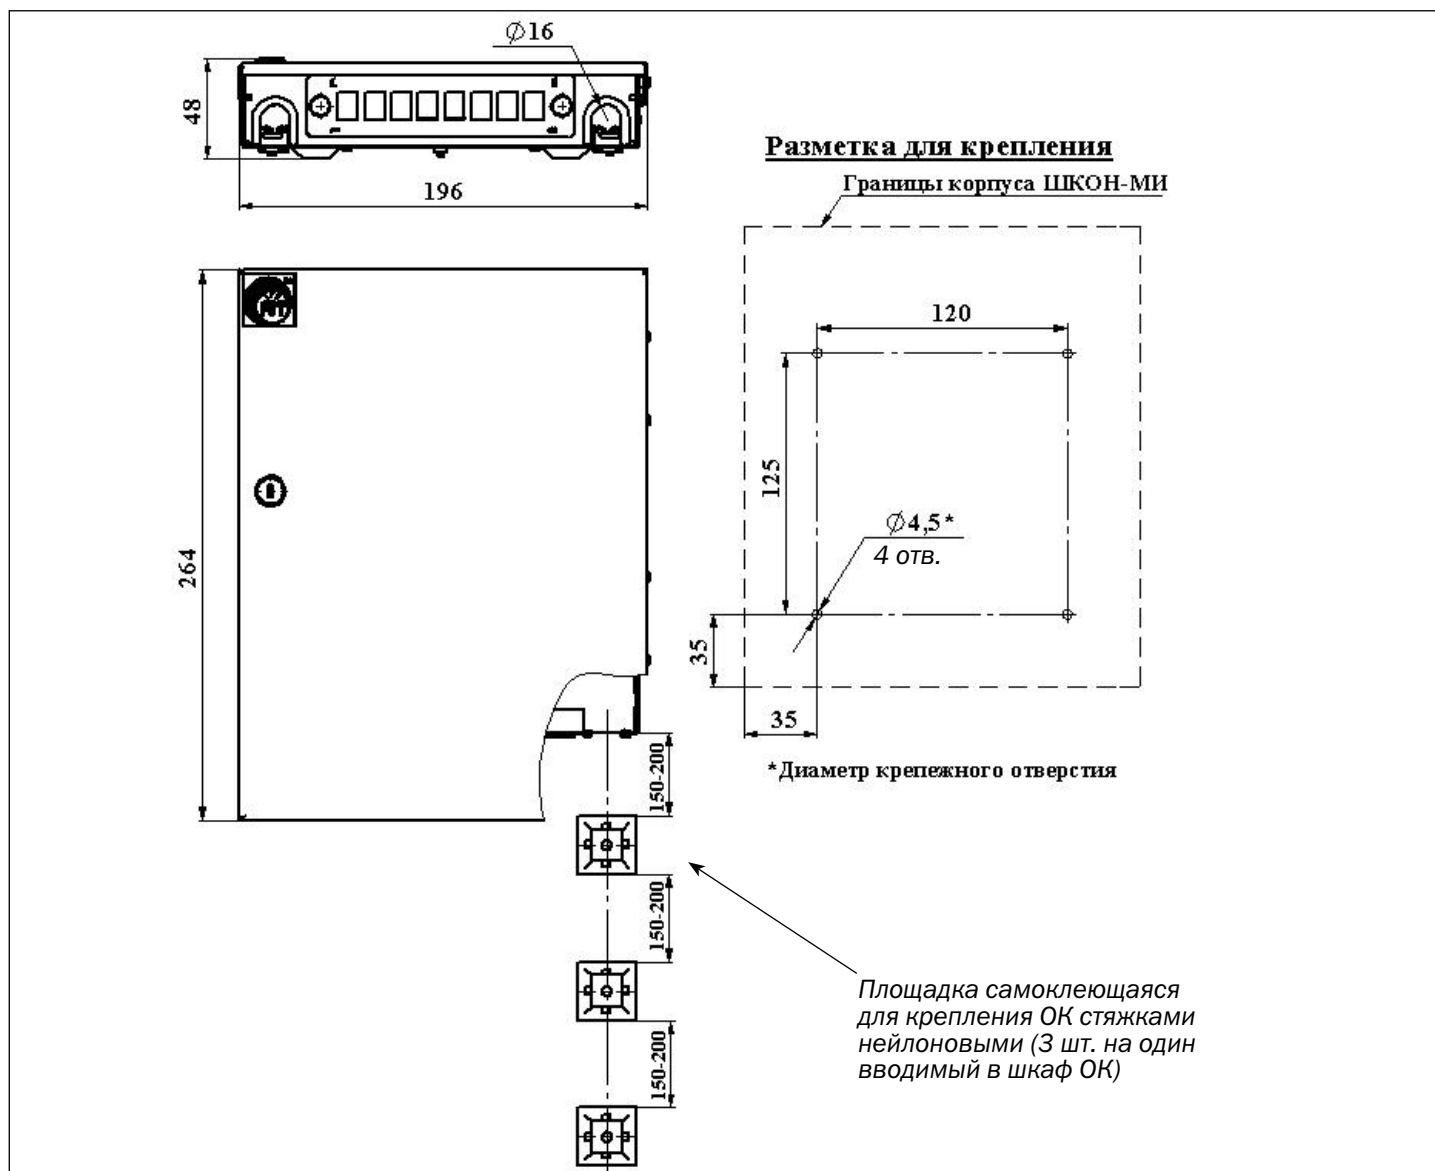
Габаритные и установочные размеры шкафа
